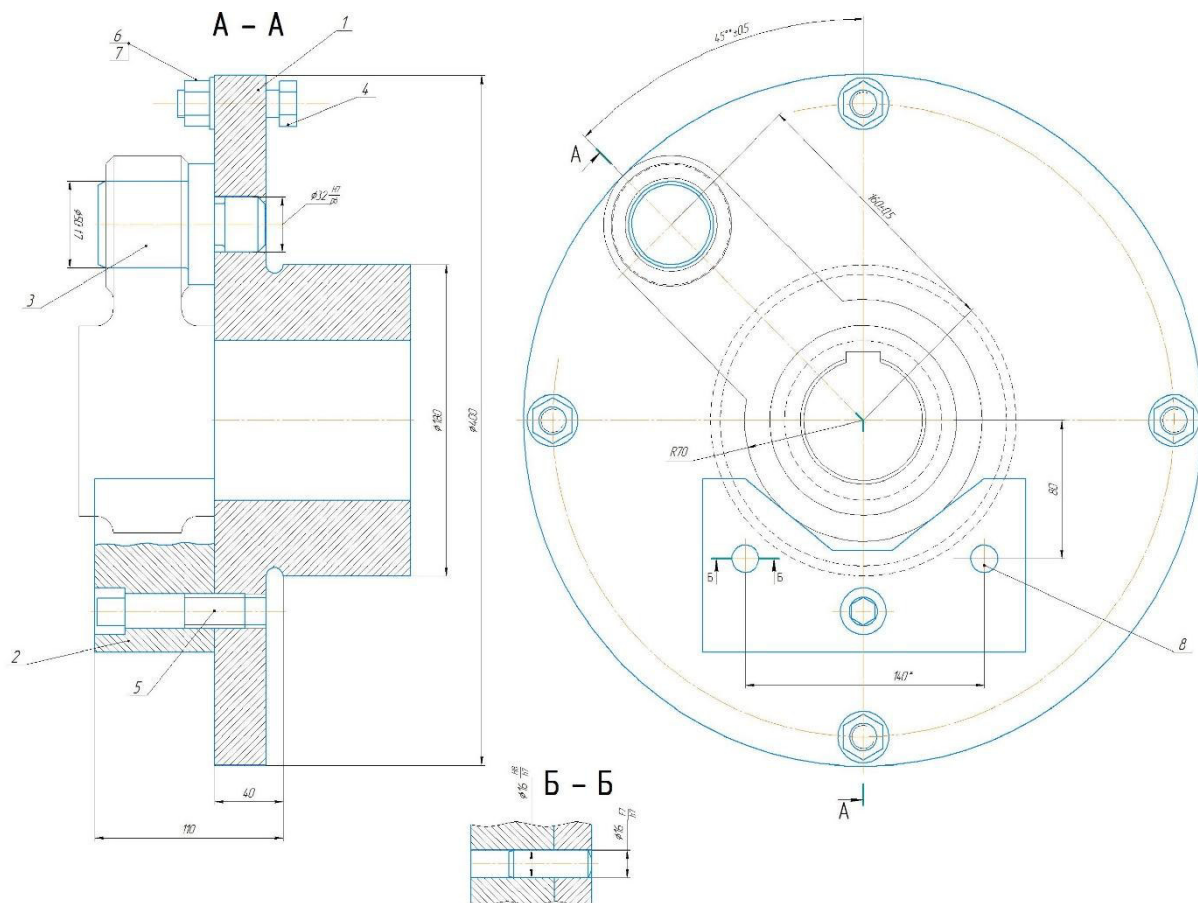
Приспособление для закрепления детали на горизонтально – протяжном станке: 1 –корпус; 2 –призма опорная; 3- палец цилиндрический; 4- болт; 5 –винт; 6- гайка; 7 –шайба; 8- штифт.
